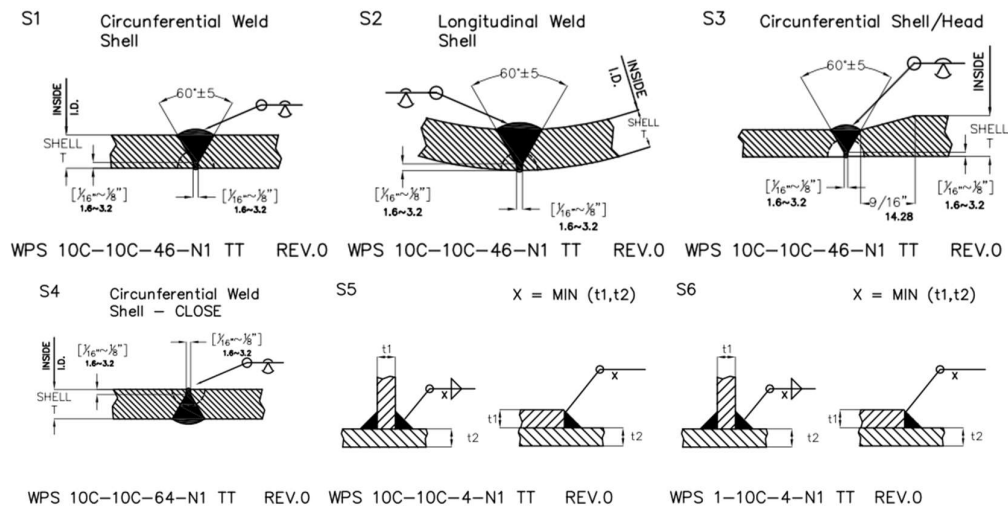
Esquemas de Tipos de Soldadura Aplicables a la Construcción del Auto Tanque
